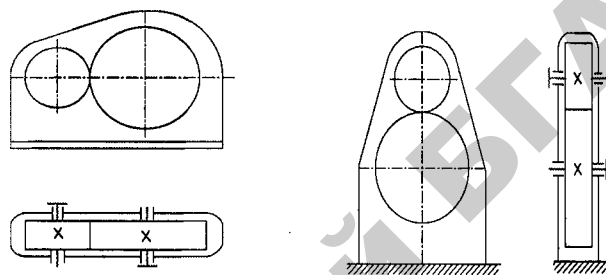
Зубчатые одноступенчатые цилиндрические редукторы
